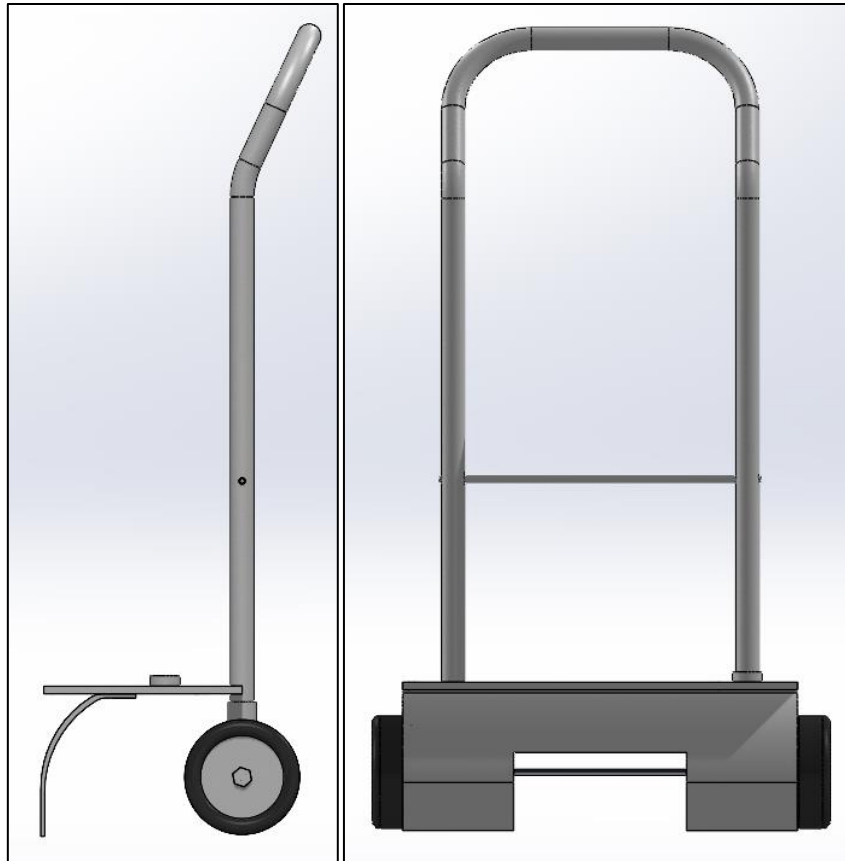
Vista lateral y alzado del conjunto carro. Fuente propia.
